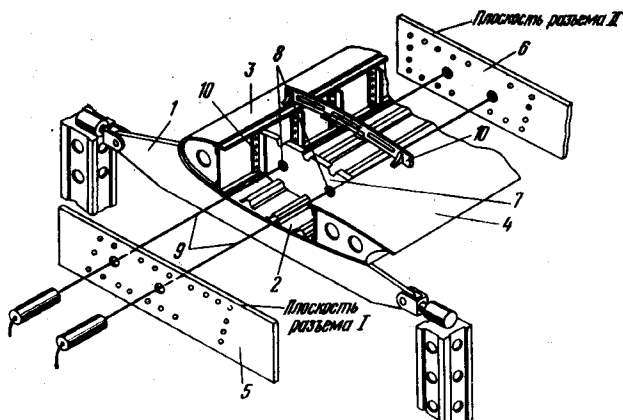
Схема сборки и контроля расположения каркасного набора крыла на базе опорных лазерных лучей:
